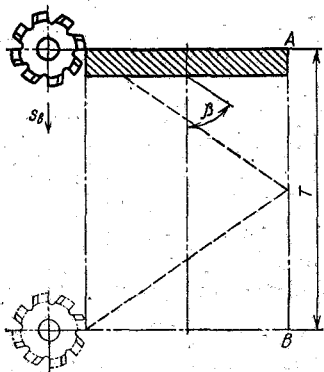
Схема нарезания косозубого колеса червячной фрезой
